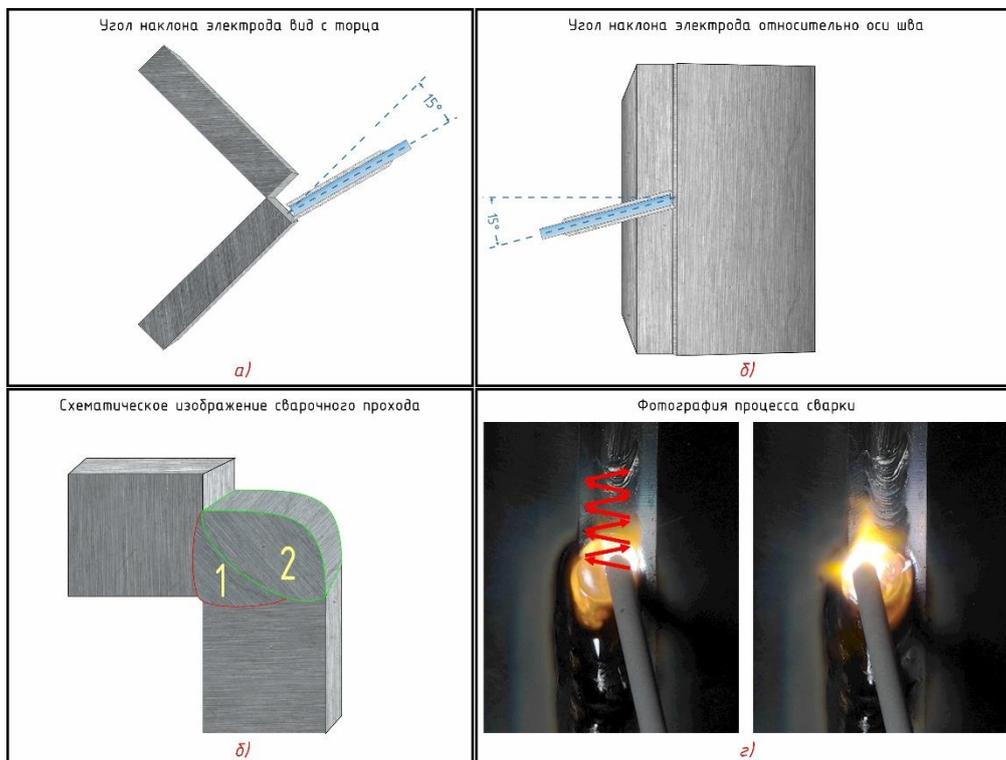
Положение электродов при сварке второго прохода
